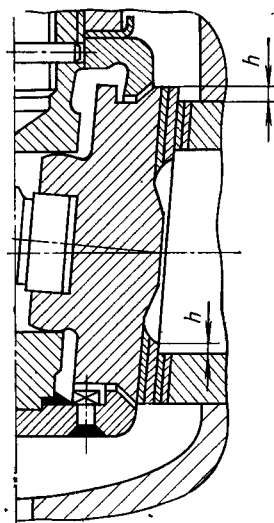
Взаимное расположение уплотнительных колец клина и корпуса задвижки после их подгонки и притирки.
